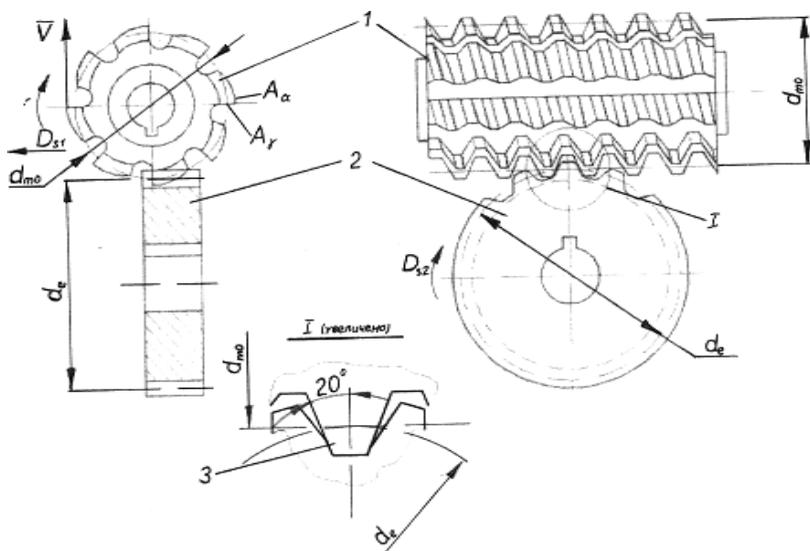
Схема нарезания зубчатого колеса червячной модульной фрезой:
